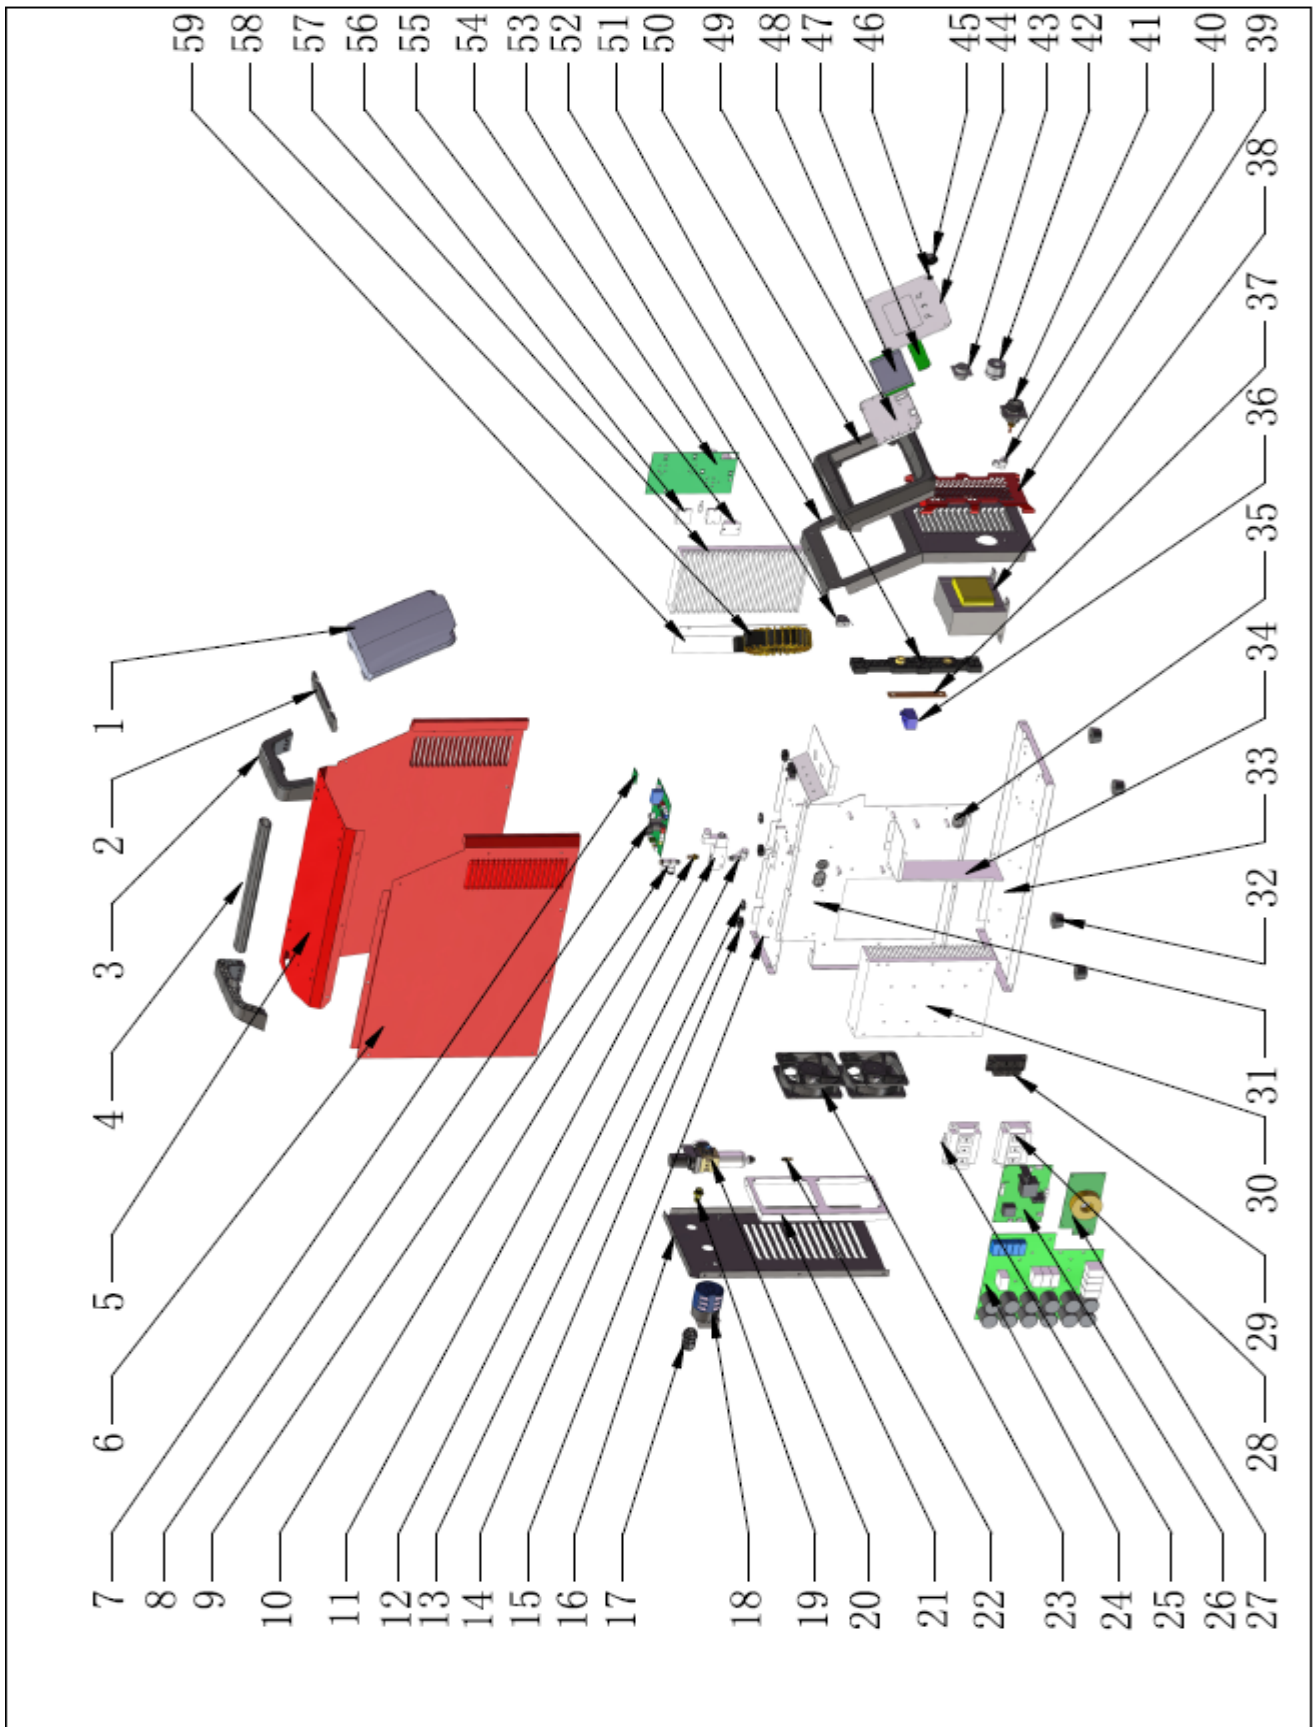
Ersatzteilzeichnung CRAFT-CUT 123 CNC LCD
